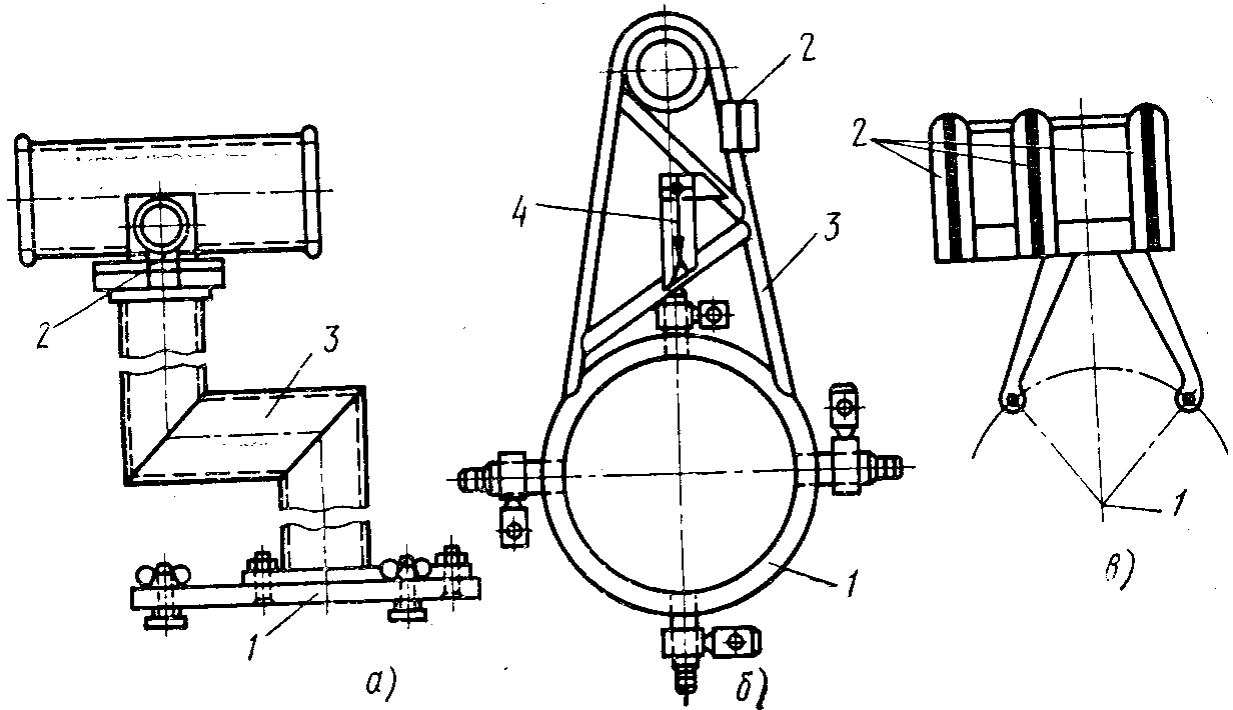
Схема контрольно-регулирующего приспособления, предназначенного для установки механизма перегрузки в линию полета:
